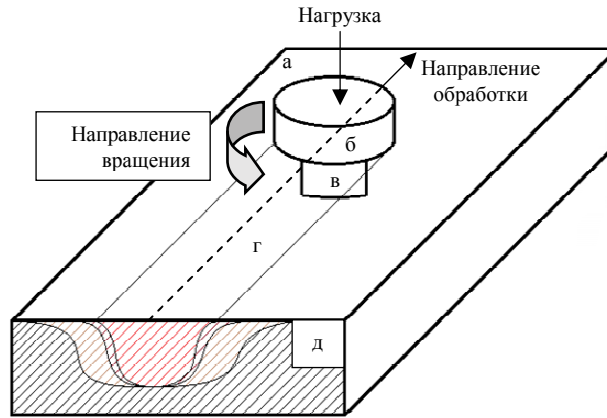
Схема процесса ФПО: а) обрабатываемый металл, б) плечи инструмента, в) пин инструмента, г) зона обработки, д) поперечное сечение обработанного материала
